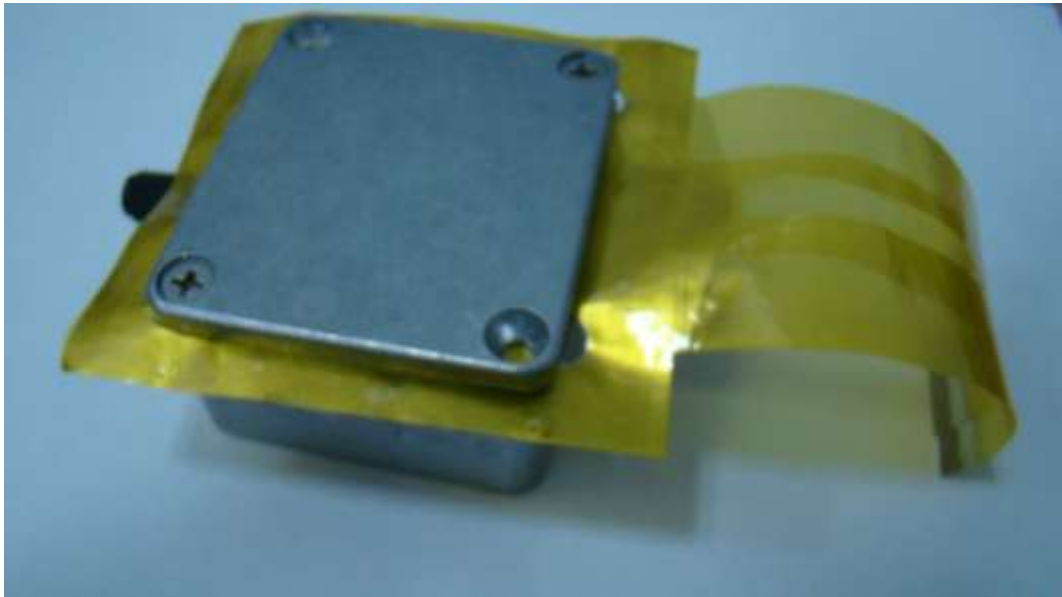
Прижимающая пластина в корпусе МКУ
